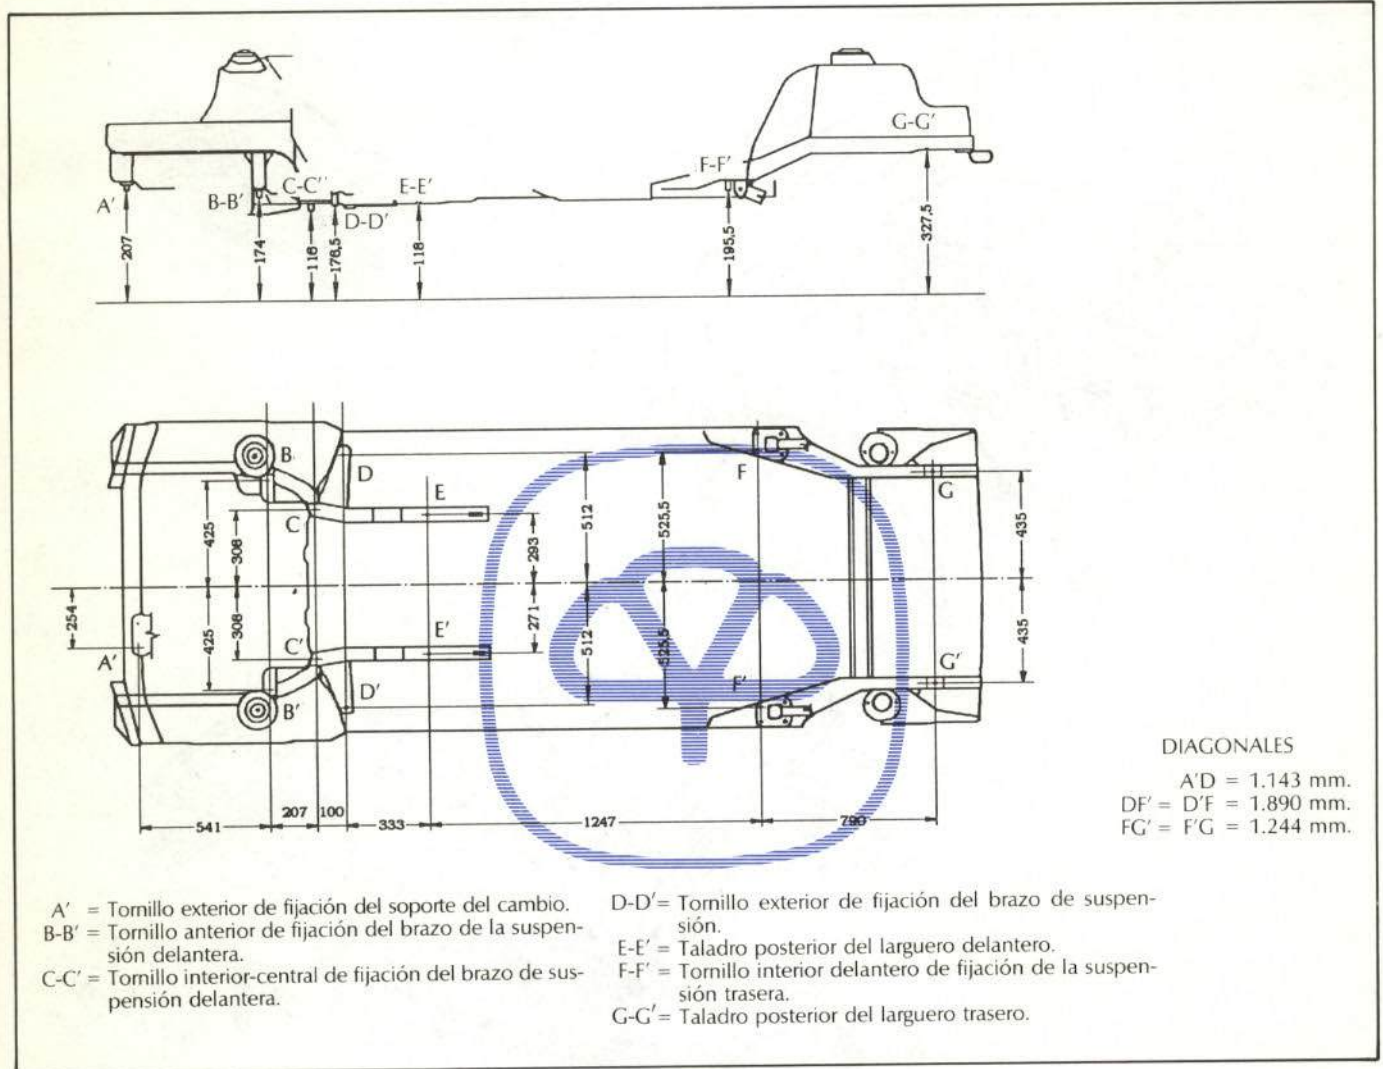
Dimensiones de la carrocería en planta y alzado.
